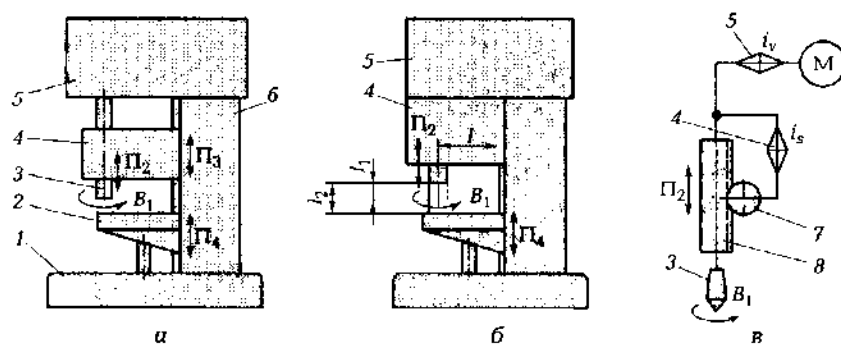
Компоновка вертикально-сверлильных станков:
